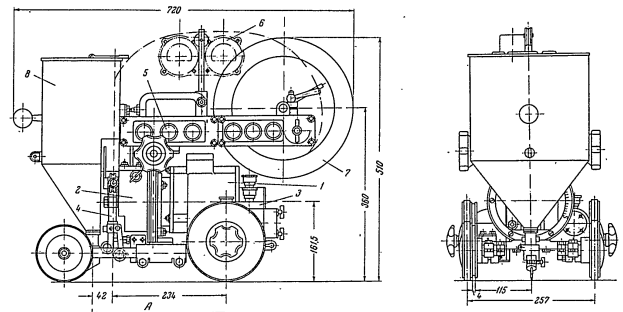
Чертеж общего вида сварочного трактора TC-17-M; А — направление движения трактора
